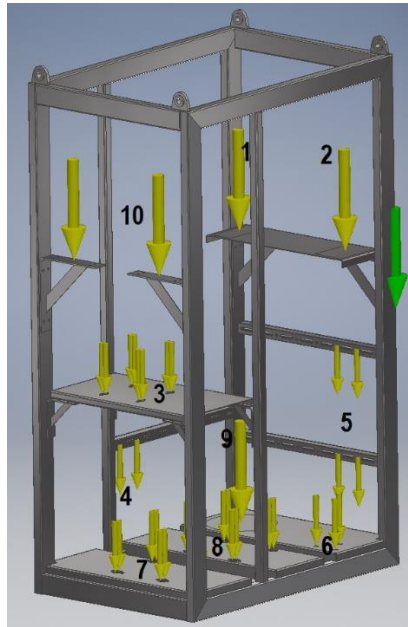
Cargas aplicadas na estrutura Mini Booster
